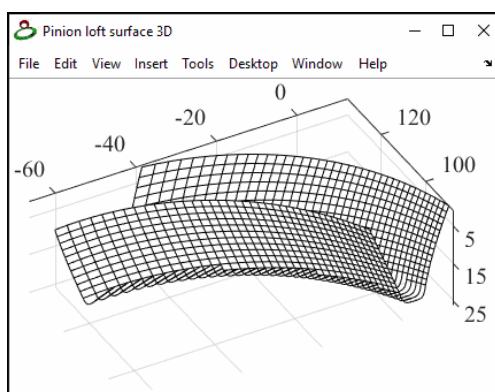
Поверхность впадины зубчатого венца шестерни спиральной конической передачи
